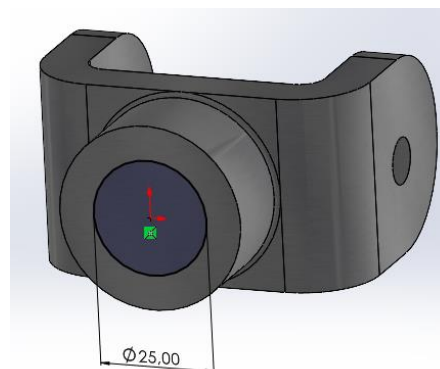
Croquis árbol de transmisión fijo de la junta cardán en SolidWorks.
